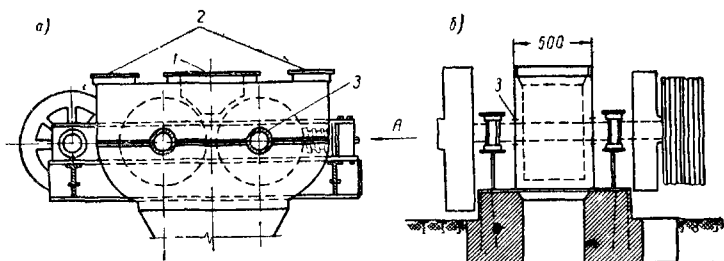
Укрытие двухвалковой дробилки типа СМ-12
